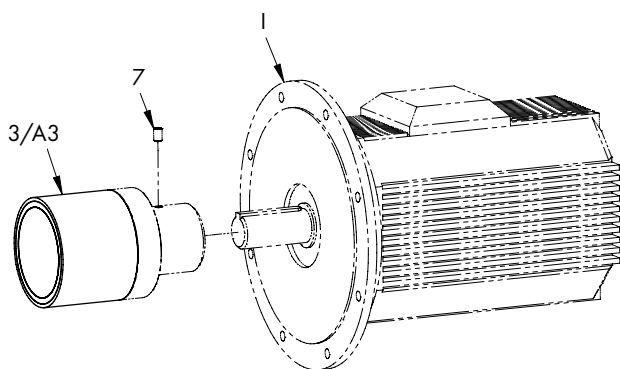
Montaggio rotore esterno sul lato motore (A5)
